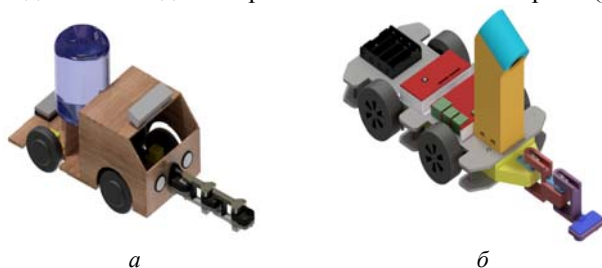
3D-модели основной (а) и портативной (б) версии
